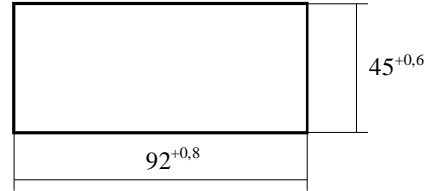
Габаритные и монтажные размеры измерительного прибора
